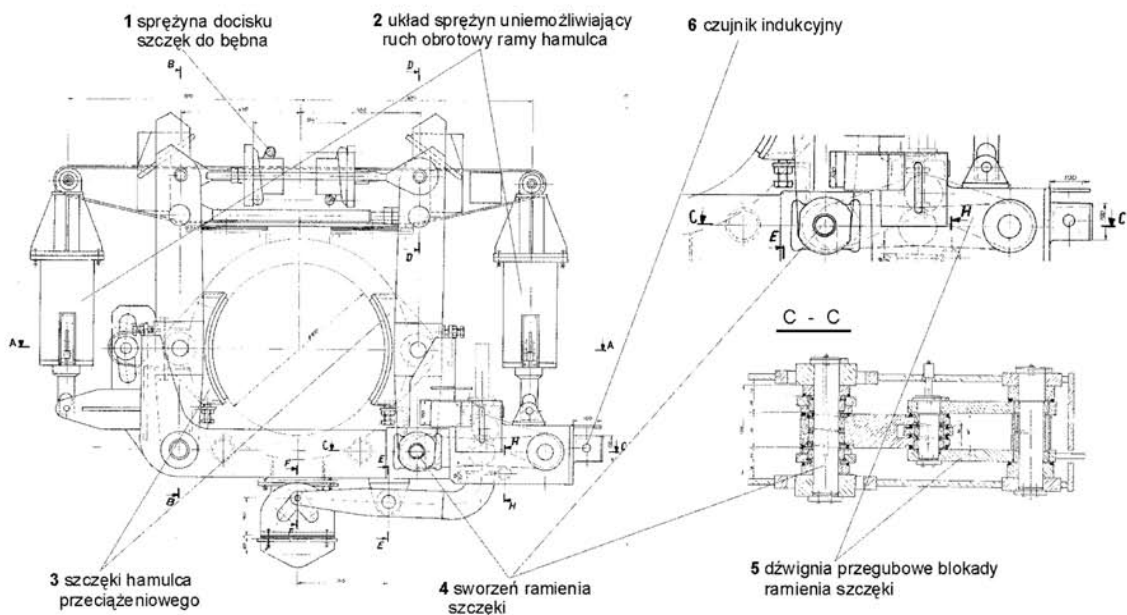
Napęd koła czerpakowego koparki SchRs 4600
